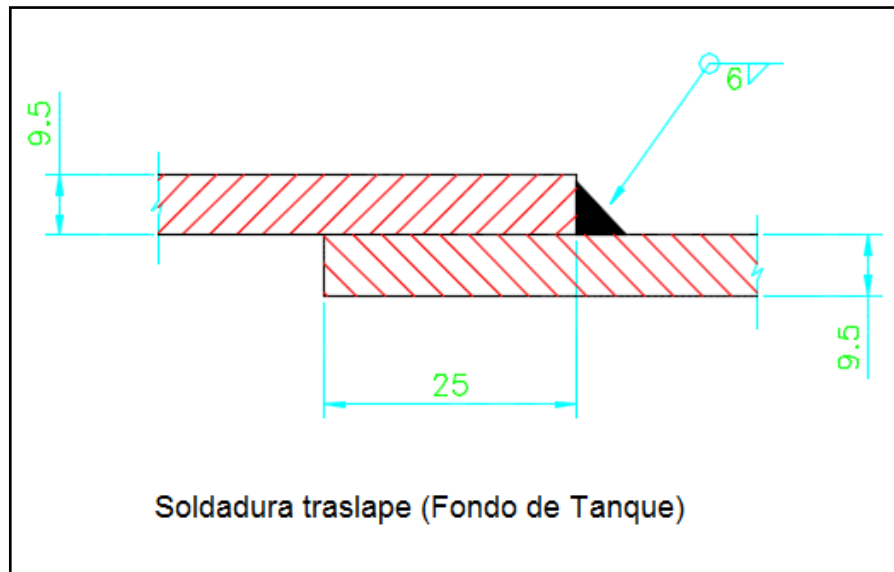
Soldadura Traslape para el fondo del tanque.
